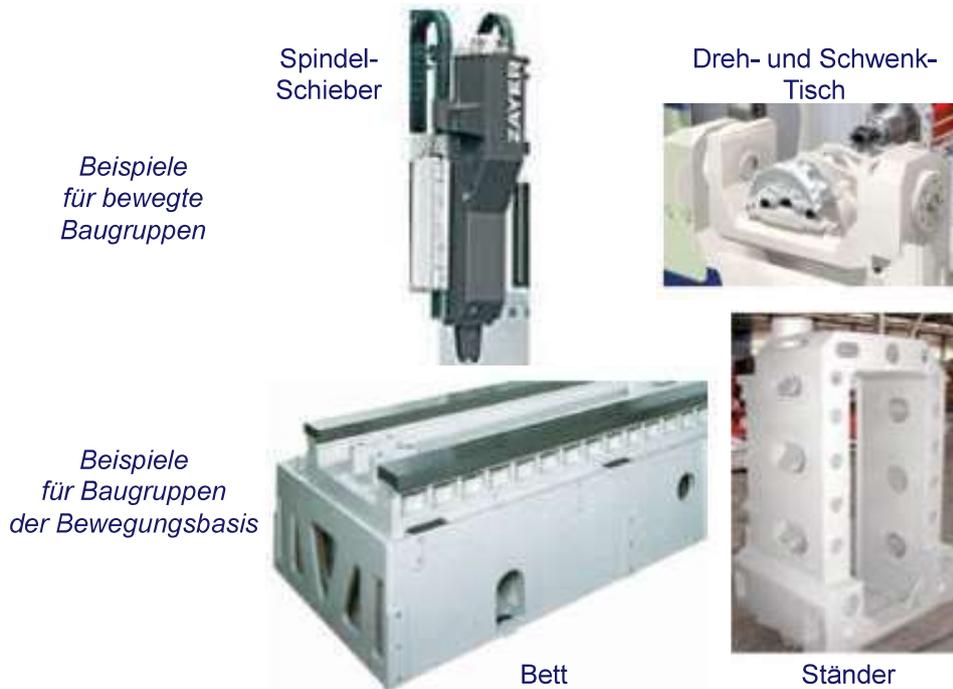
Beispiele für Gestellbaugruppen von Werkzeugmaschinen
